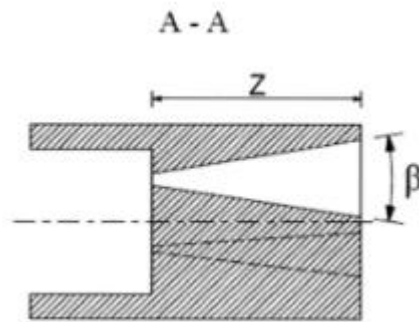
Струменеутворювальна віялова насадка (поздовжній переріз)
